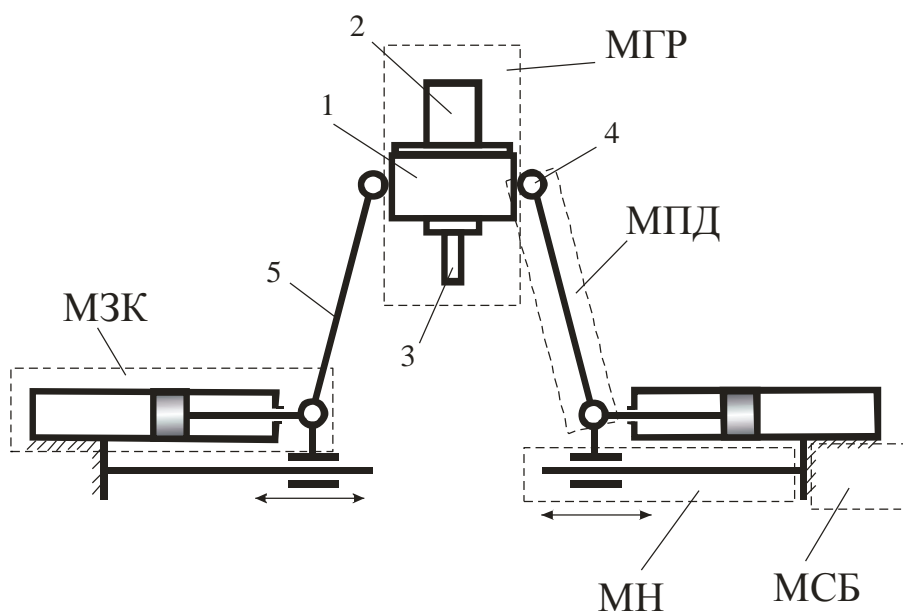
Механізм із зміною координат опорних шарнірів: 1 – виконавчий орган; 2 – привод головного руху; 3 – інструмент; 4 – шарнір; 5 – кінематична ланка постійної довжини
